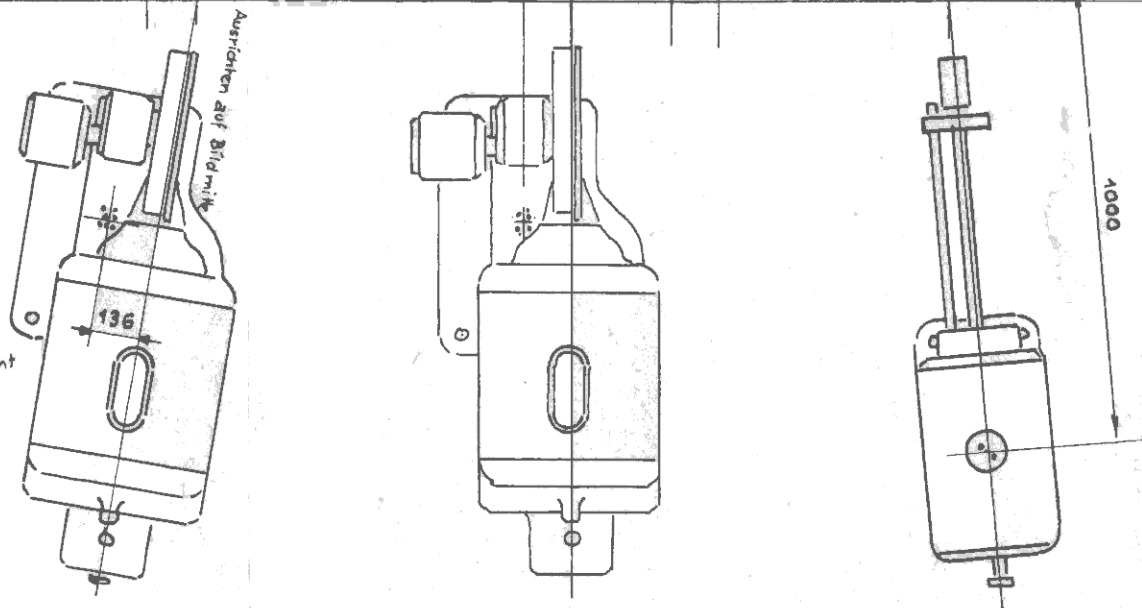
Einbauplan für 2 Bauer-B 8-Projektoren mit Hochleistungslampe HI 75 und für 1 Bauer-Dia-Projektor.
